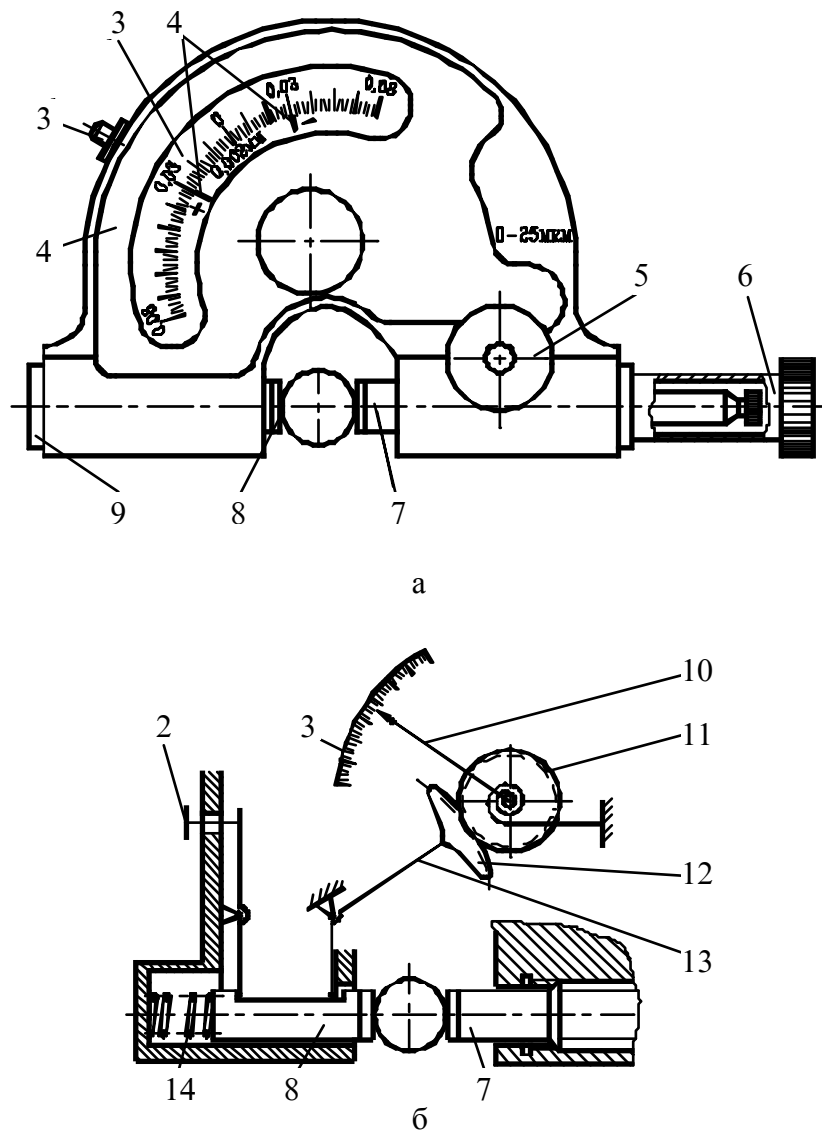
Рычажная скоба: а – общий вид, б – кинематическая схема
